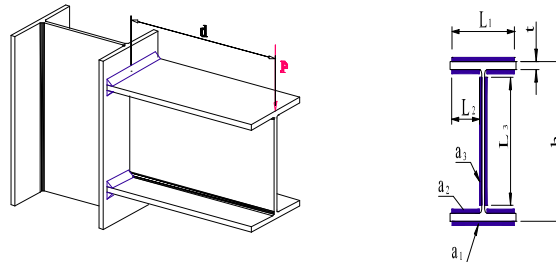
Uniones soldadas planas sometidas a flexión.
